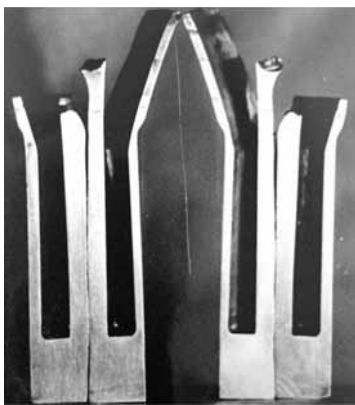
Деталь, изготовленная из биметаллической заготовки
